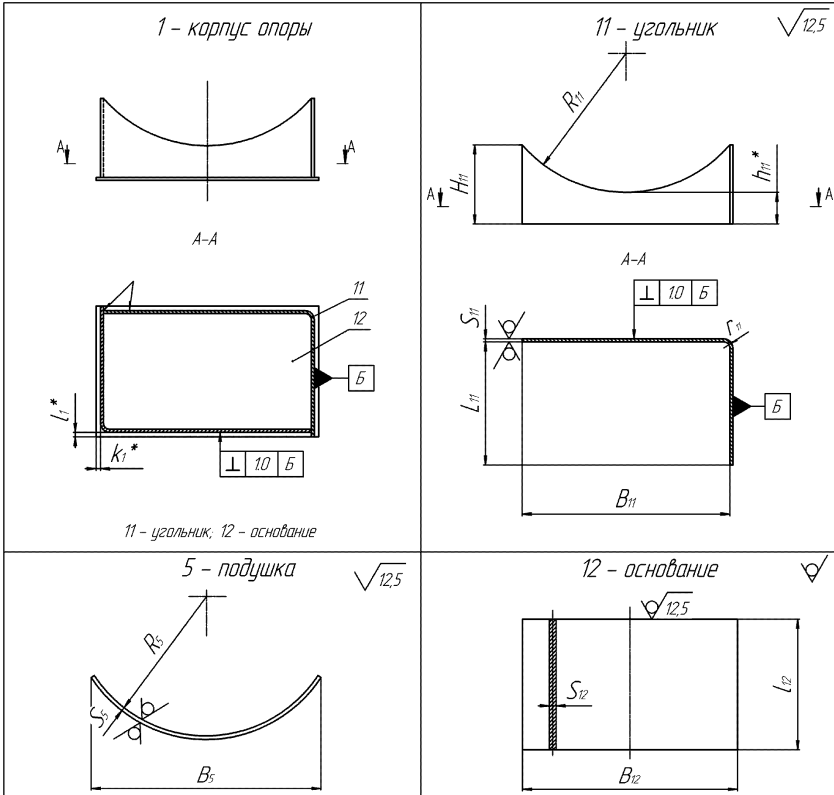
Детали изделий 02-XXXX-S-1C-XX-A,
